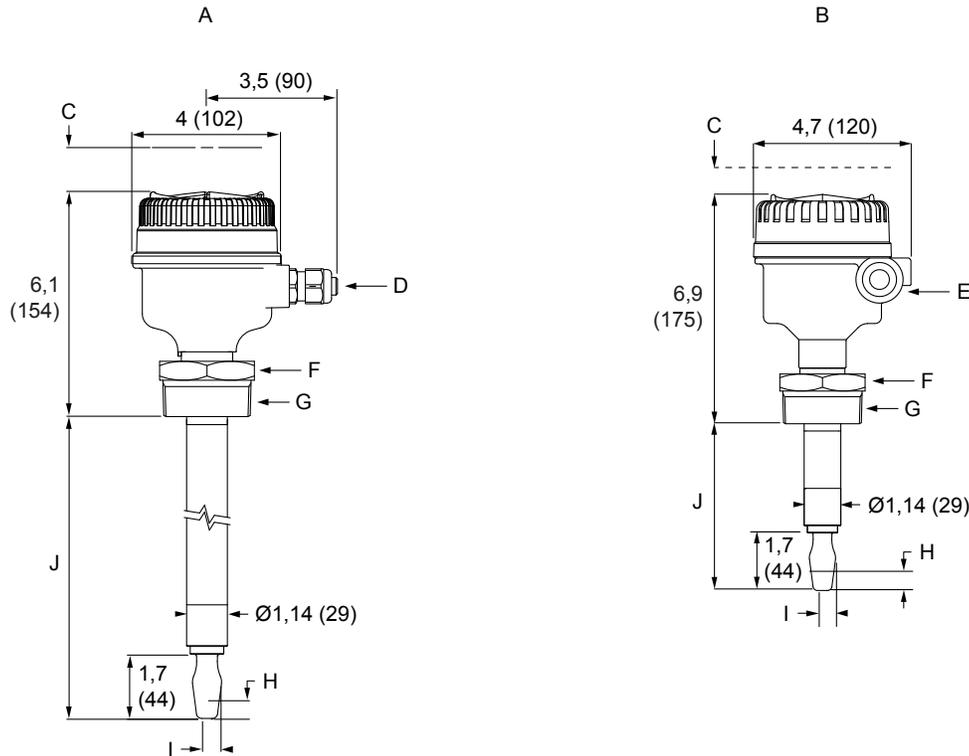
3/4 und 1 in. Gewindemontage (mit Verlängerung)
